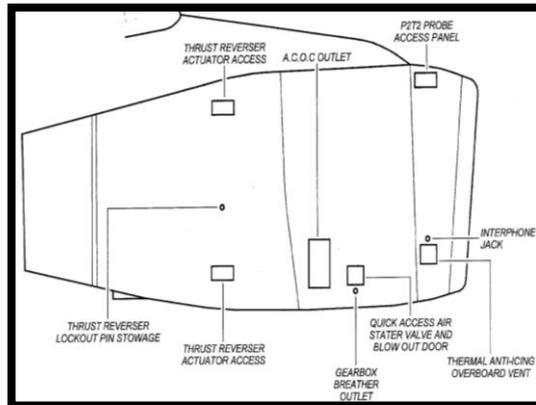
Puertas de Acceso del lado Izquierdo del Motor V 2500
